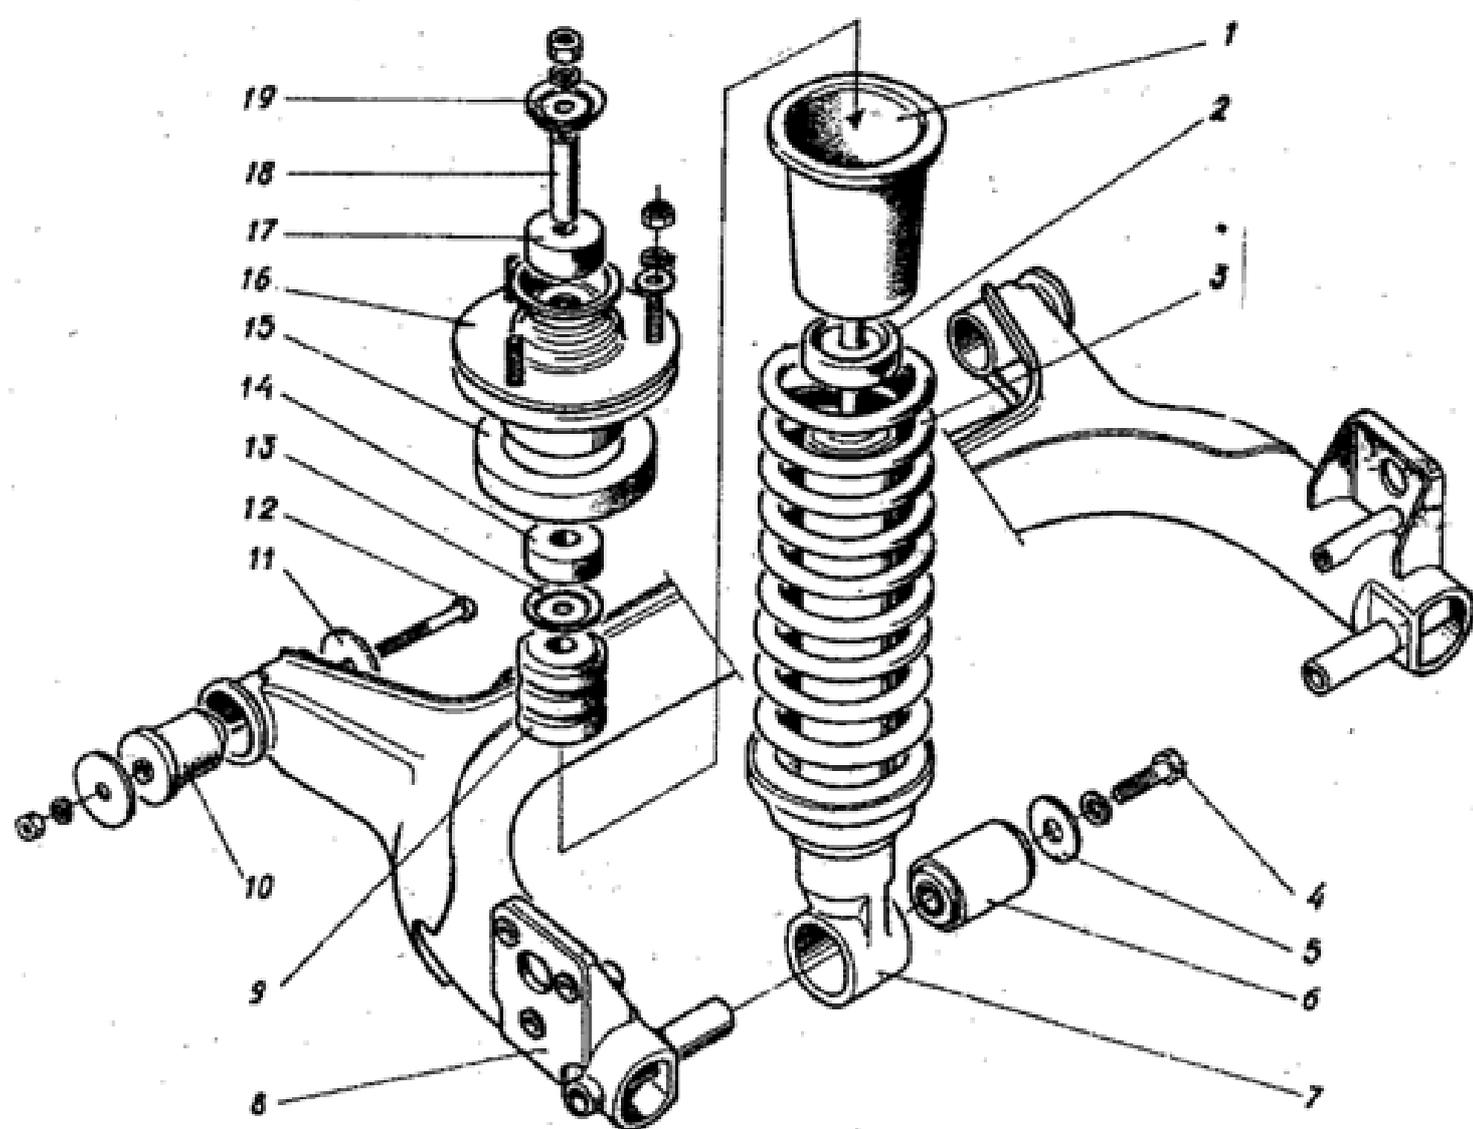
Детали задней подвески: 1 - чехол; 2 - обойма буфера; 3 - пружина; 4 - болт крепления нижнего шарнира; 5 - шайба; 6 - сайлентблок; 7 - амортизатор; 8 - балка; 9 - буфер; 10 - сайлентблок балки; 11 - шайба; 12 - болт крепления балки; 13 - обойма; 14 - подушка амортизатора; 15 - прокладка изоляционная; 16 - опора пружины; 17 - подушка амортизатора; 18 - втулка; 19 - обойма.
